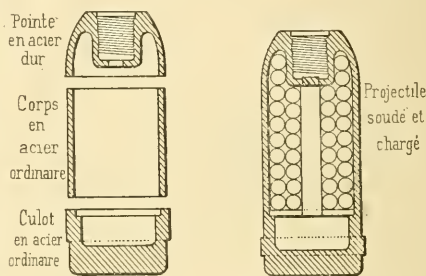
Fabrication d'obus soudés par le procédé Thomson.
